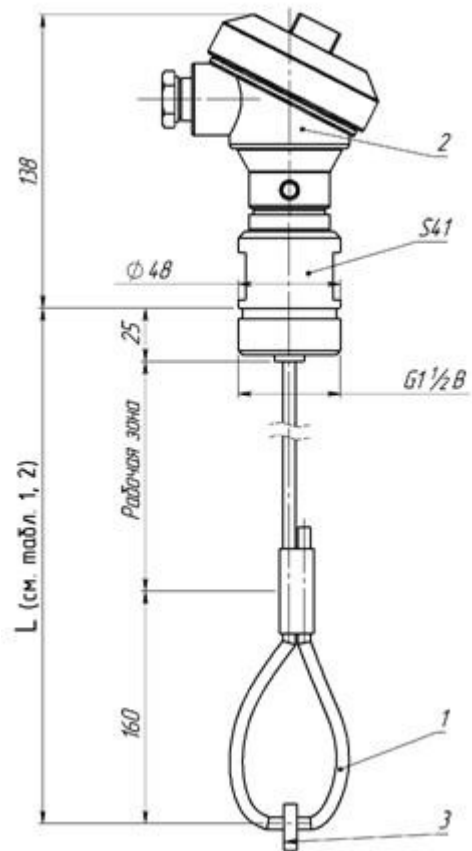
Габаритные и установочные размеры преобразователя передающего
